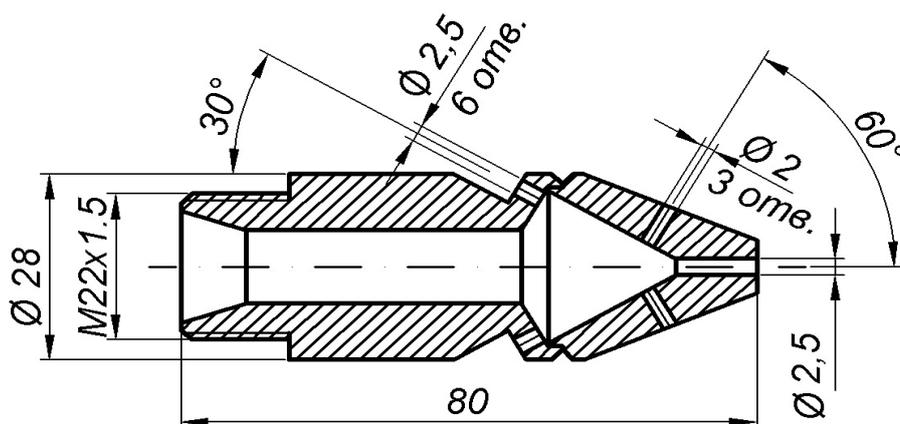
Конструкция промывочной насадки, применяемой в устройстве промывки дренажа УПД-120
